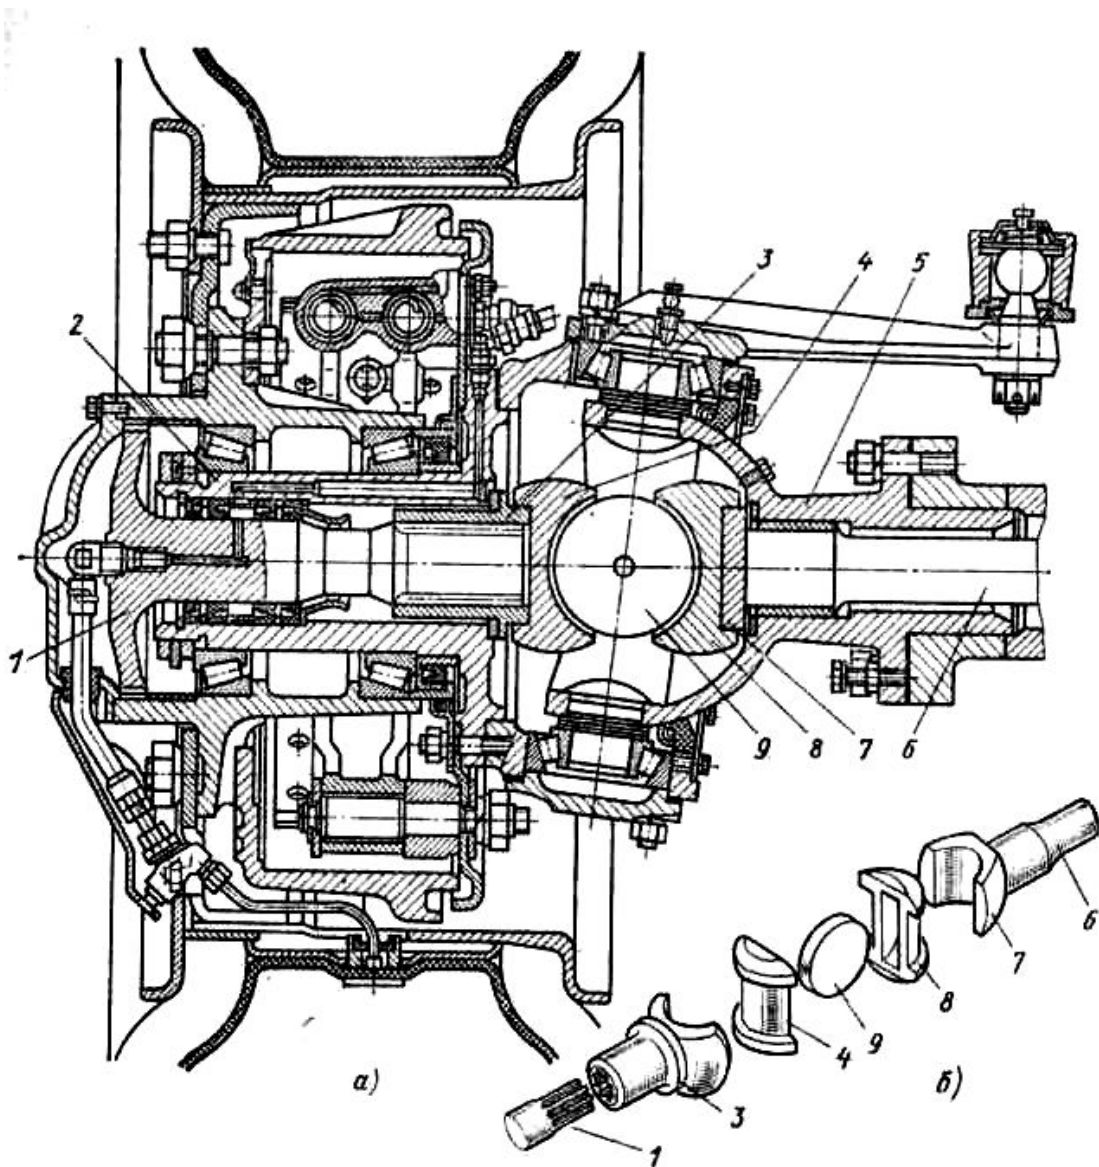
Привод переднего колеса автомобиля с кулачковым карданным шарниром
